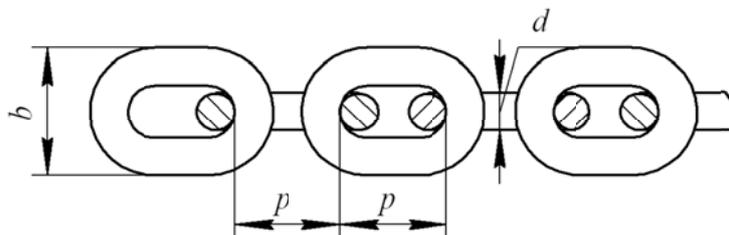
Сварная круглозвенная цепь:
